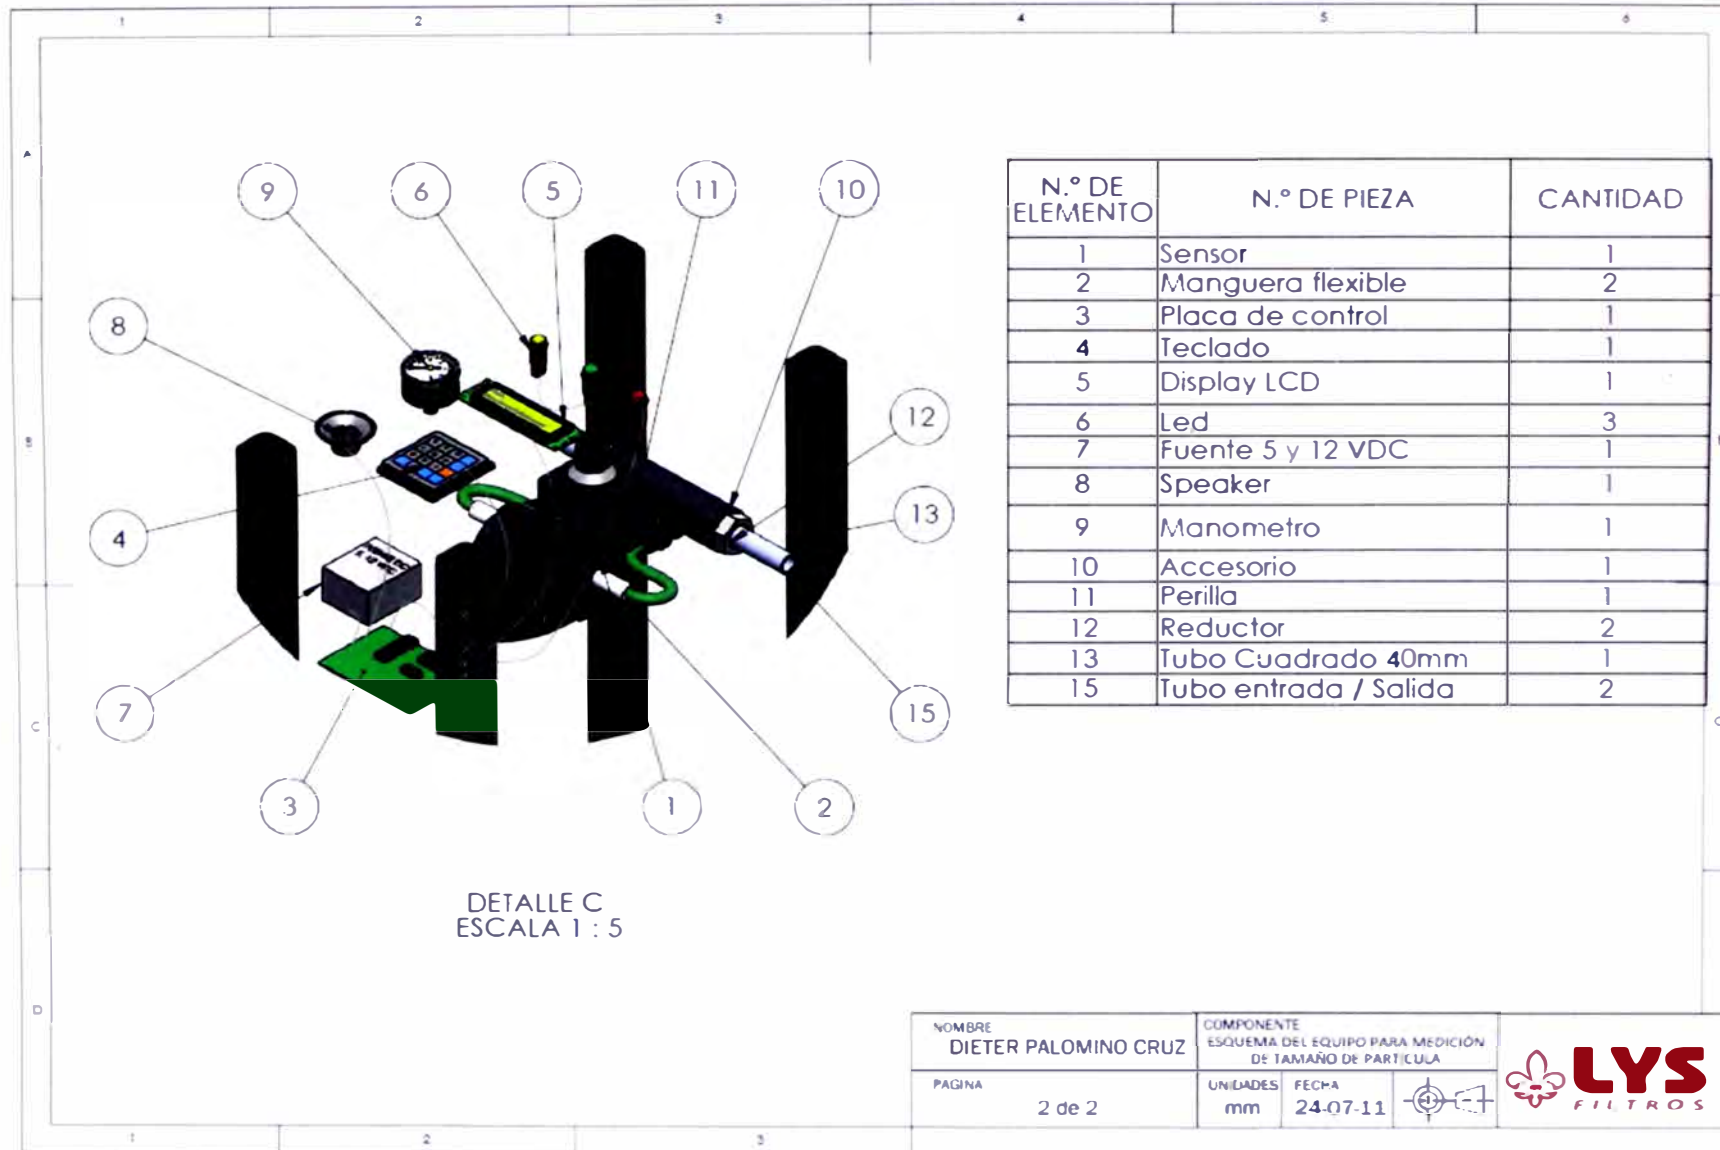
, Despiece del equipo. Fuente: diseño propio
